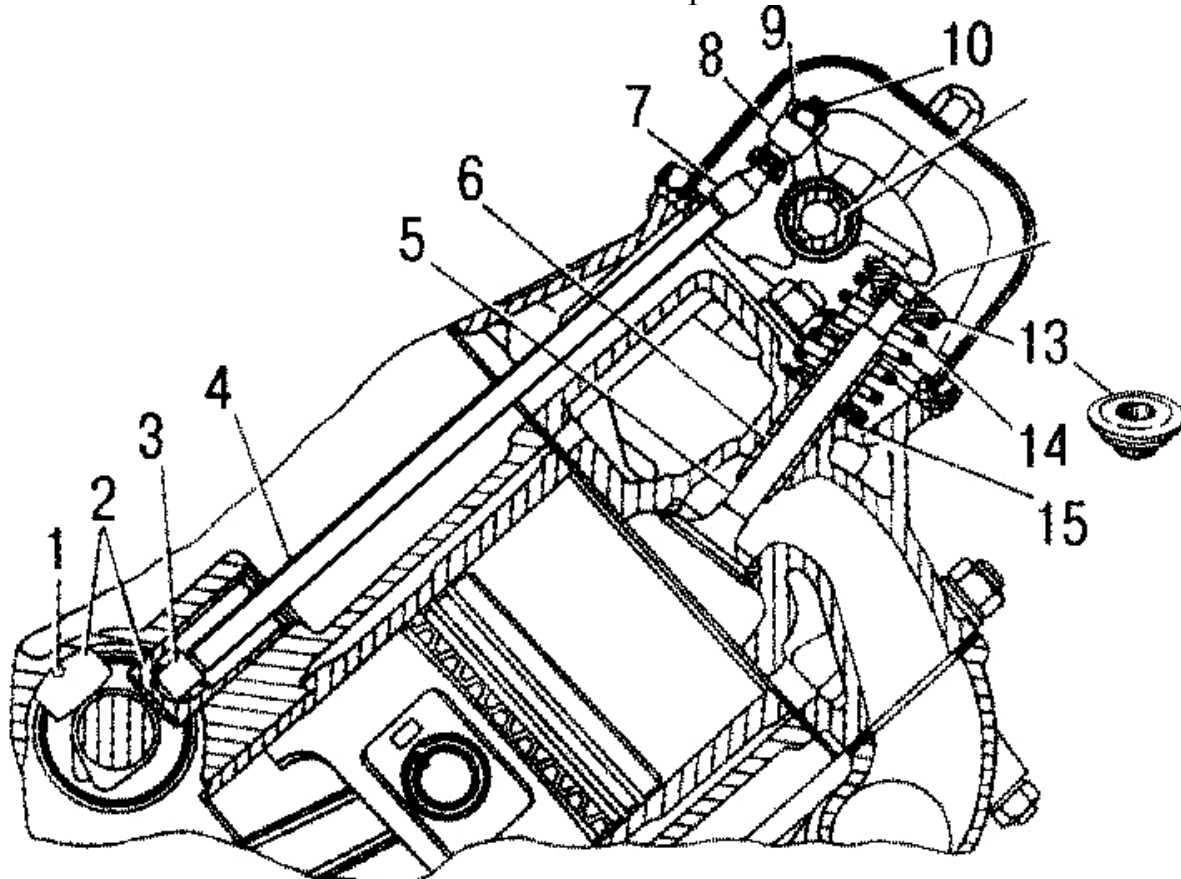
Механизм привода клапанов: 1 - отверстие для выхода масла; 2 - толкатель; 3,7- наконечники штанги; 4 - штанга; 5 - клапан; 6 - направляющая втулка; 8 - коромысло; 9 - контргайка; 10 - регулировочный винт; 11 - ось коромысел; 12 - сухари; 13 - тарелка; 14- пружина; 15 - опорная шайба
